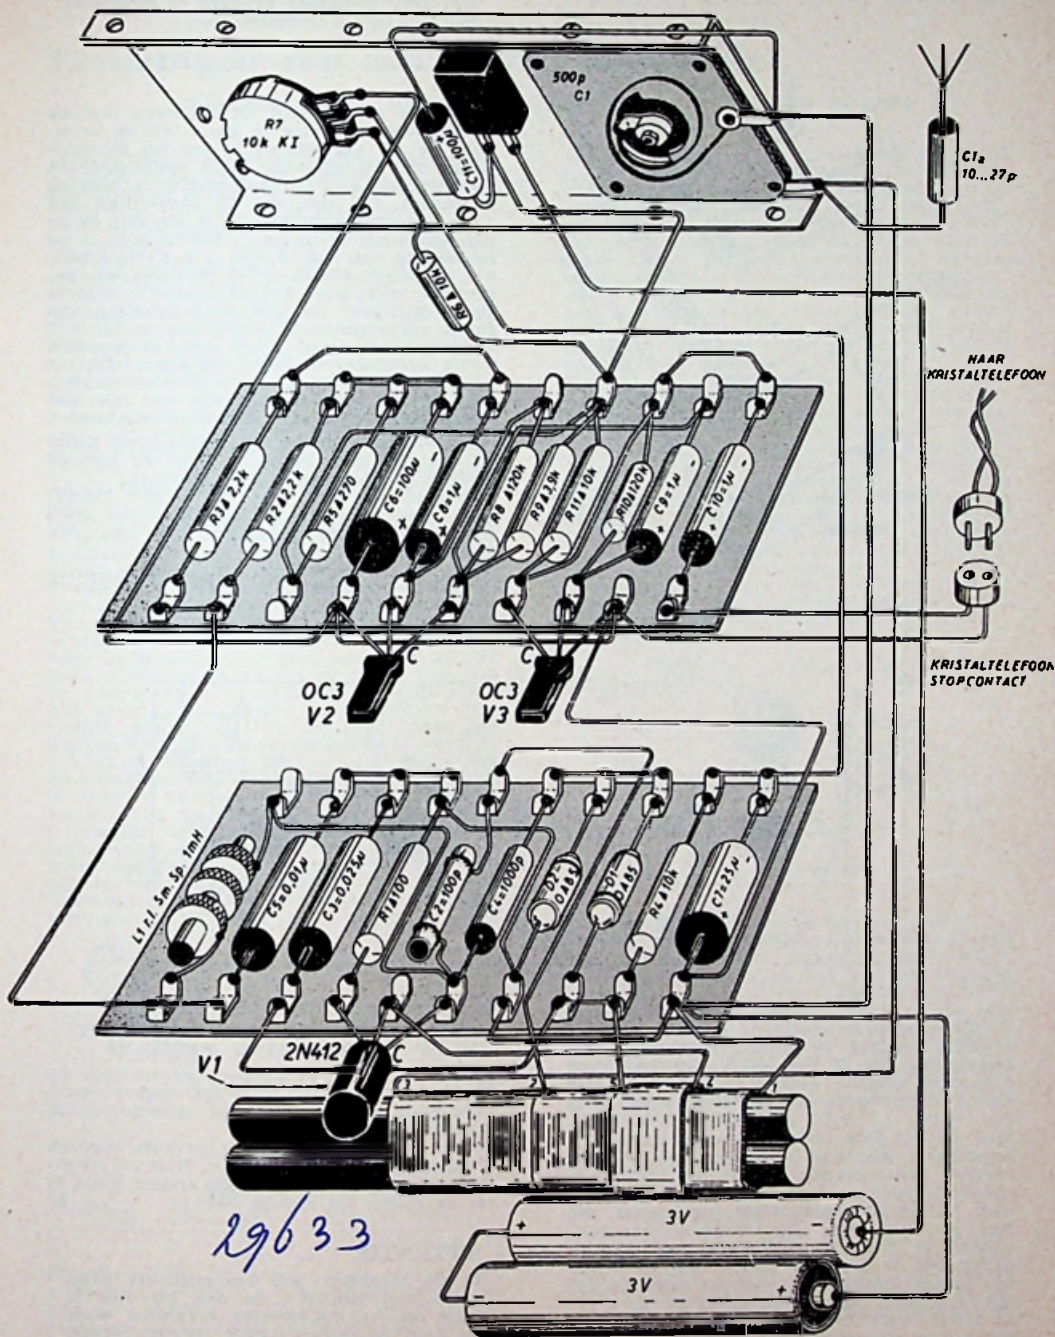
MONTAGEPLAN VOOR DE REFLEXONTVANGER
